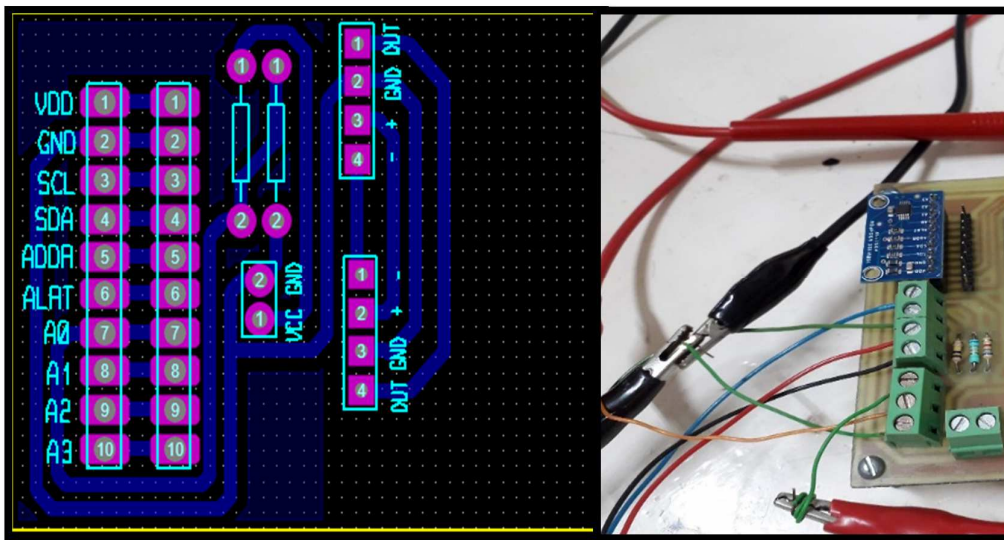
Elaboración de pistas y PCB para ADC y divisor de voltaje. Fuente: Autor
